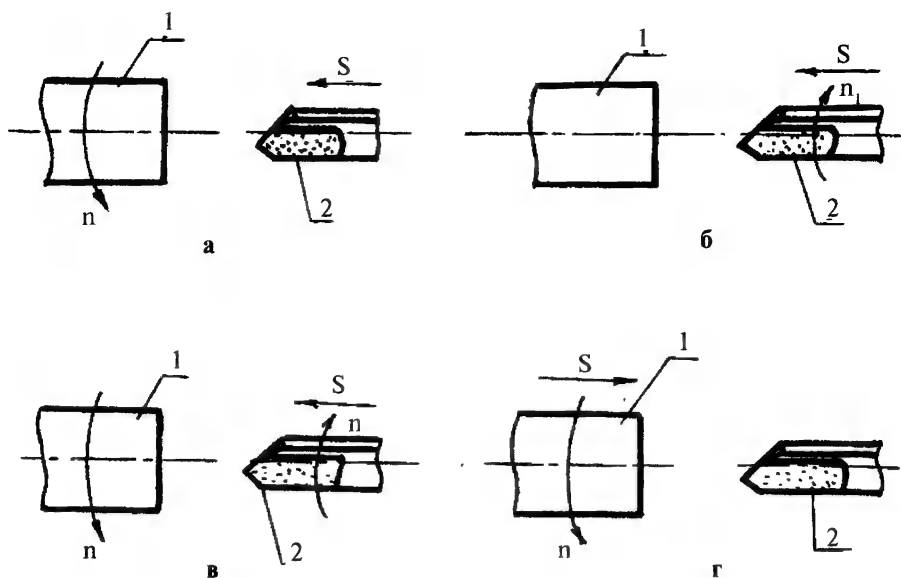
Схемы глубокого сверления: 1 - деталь, 2 - инструмент
